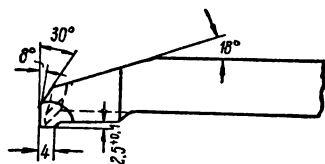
Комбинированный резец для растачивания, подрезания торцов и прорезания канавок.
